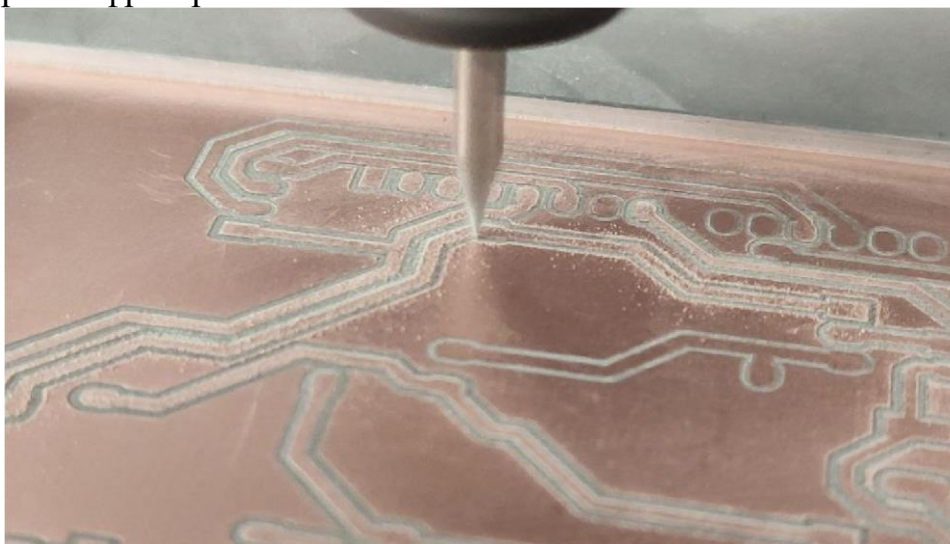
Метод фрезеровки: процесс фрезеровки платы
